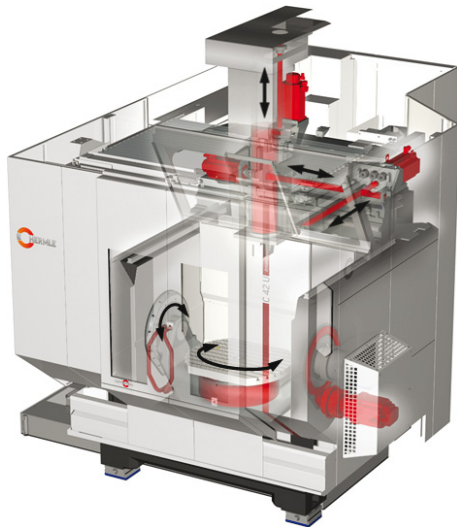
Elektrische Vorschubantriebe und Hauptantrieb in Werkzeugmaschinen (© Hermle AG, 5-Achsen Bearbeitungszentrum)
